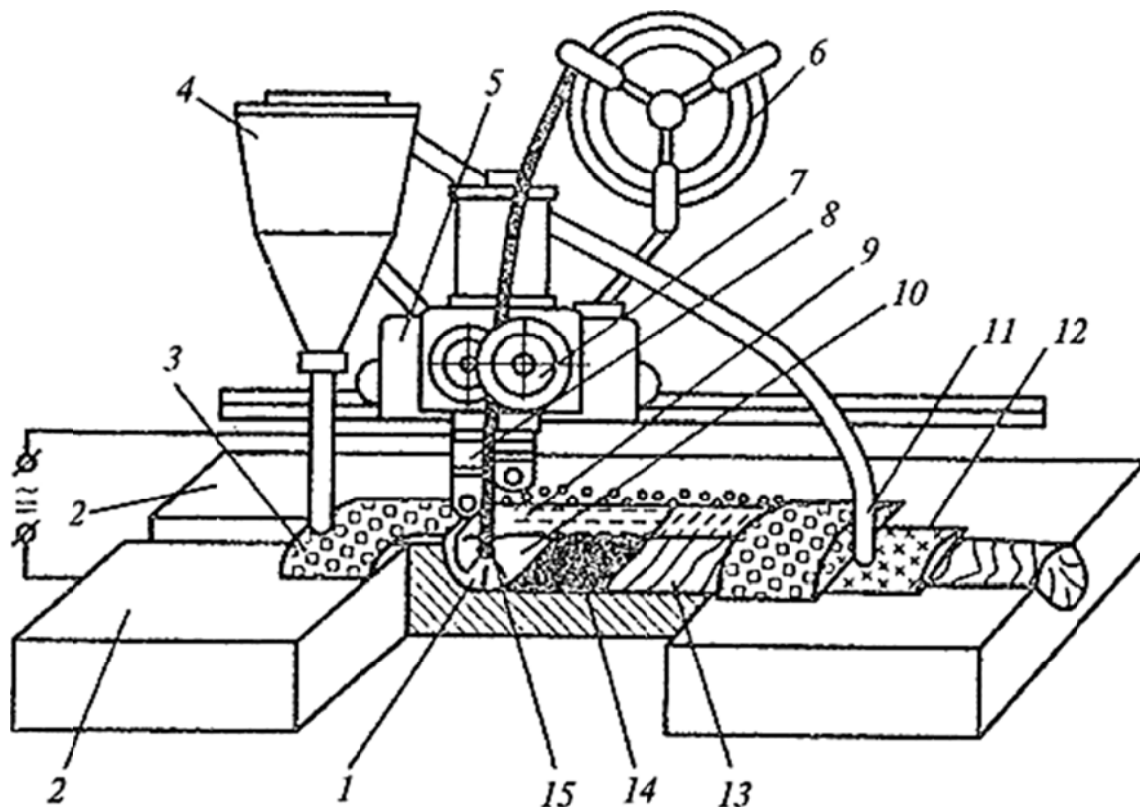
Схема автоматической сварки под флюсом:
